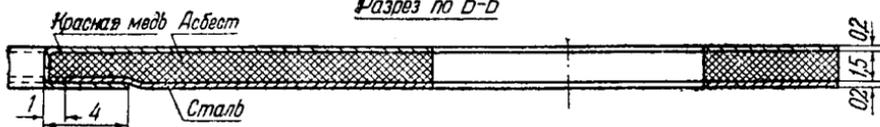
Дет. № А10—12-02. Прокладка корпуса всасывающего коллектора
